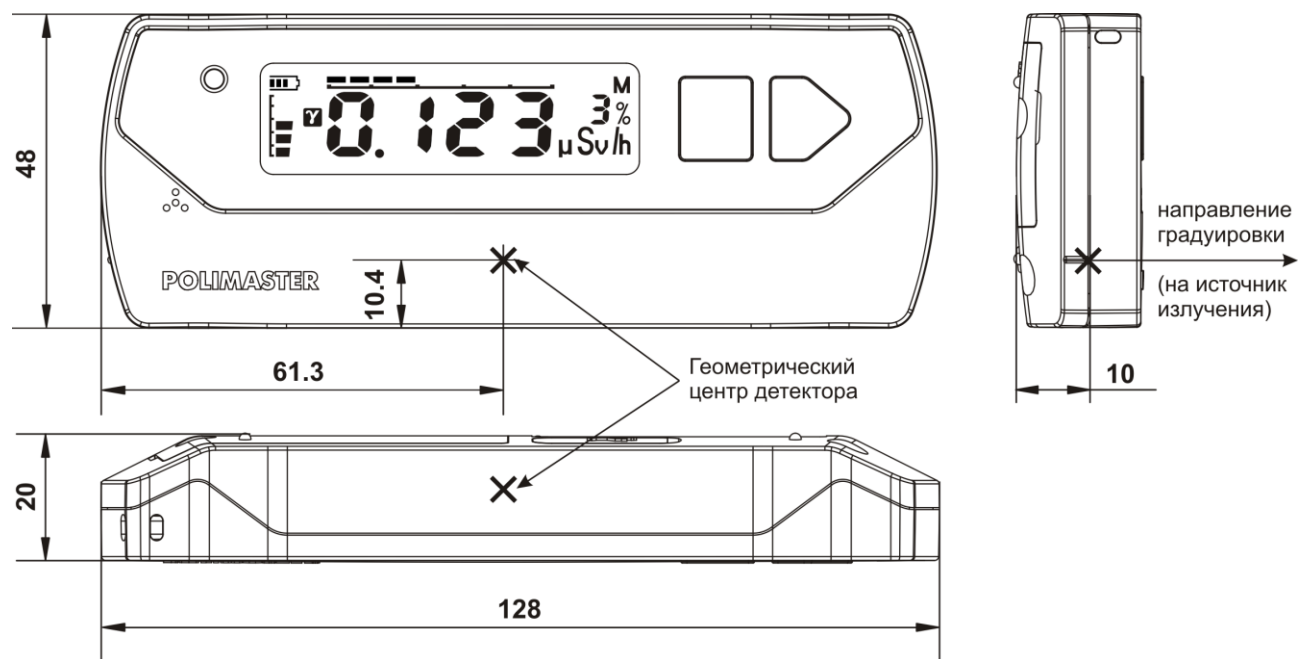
Габаритные размеры, расположение геометрического центра детектора прибора, направление градуировки
